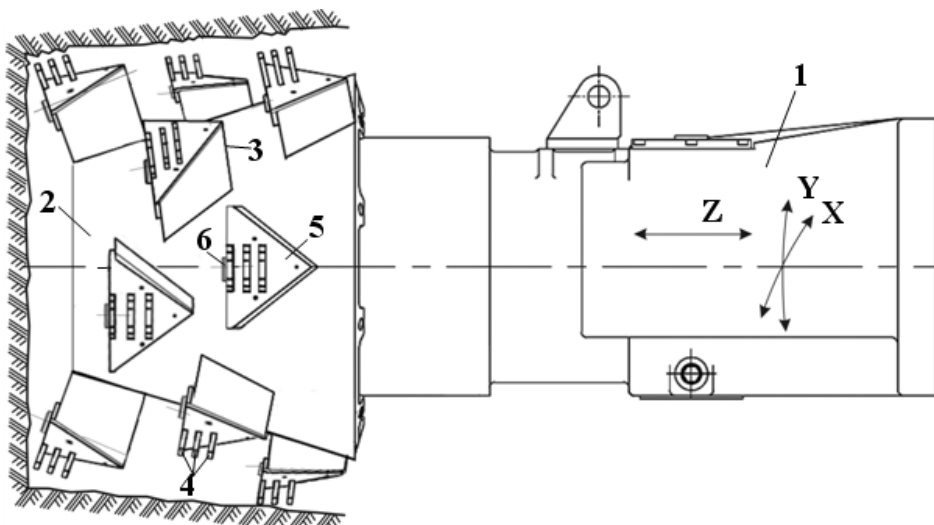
Конструкция исполнительного органа с трехгранными призмами и реверсивными режущими инструментами
